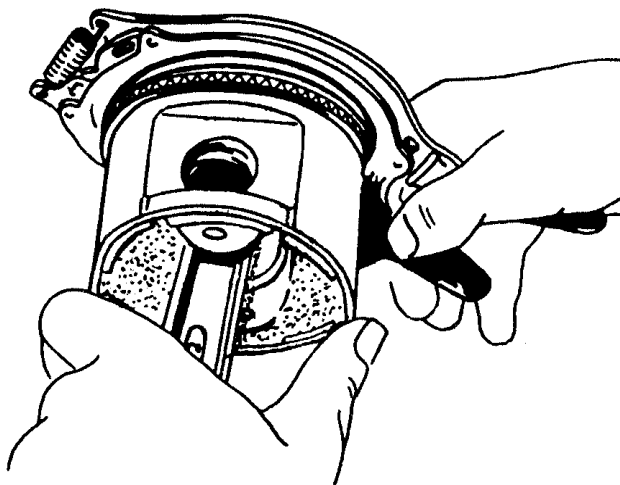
Снятие поршневых колец с поршня приспособлением 5-У-11388
